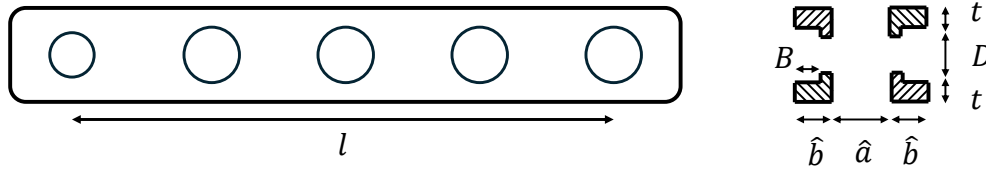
Bras de levier : vue de côté et vue en coupe de sa section
